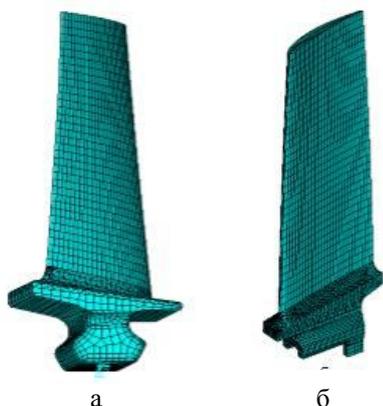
Конечно-элементная модель лопатки 3-й ступени компрессора низкого давления (а) и 6-й ступени компрессора высокого давления (б)
